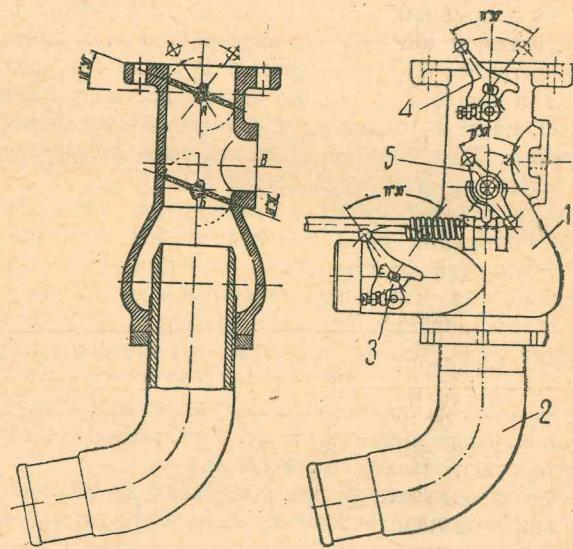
Смеситель НАТИ для двигателя ГАЗ
